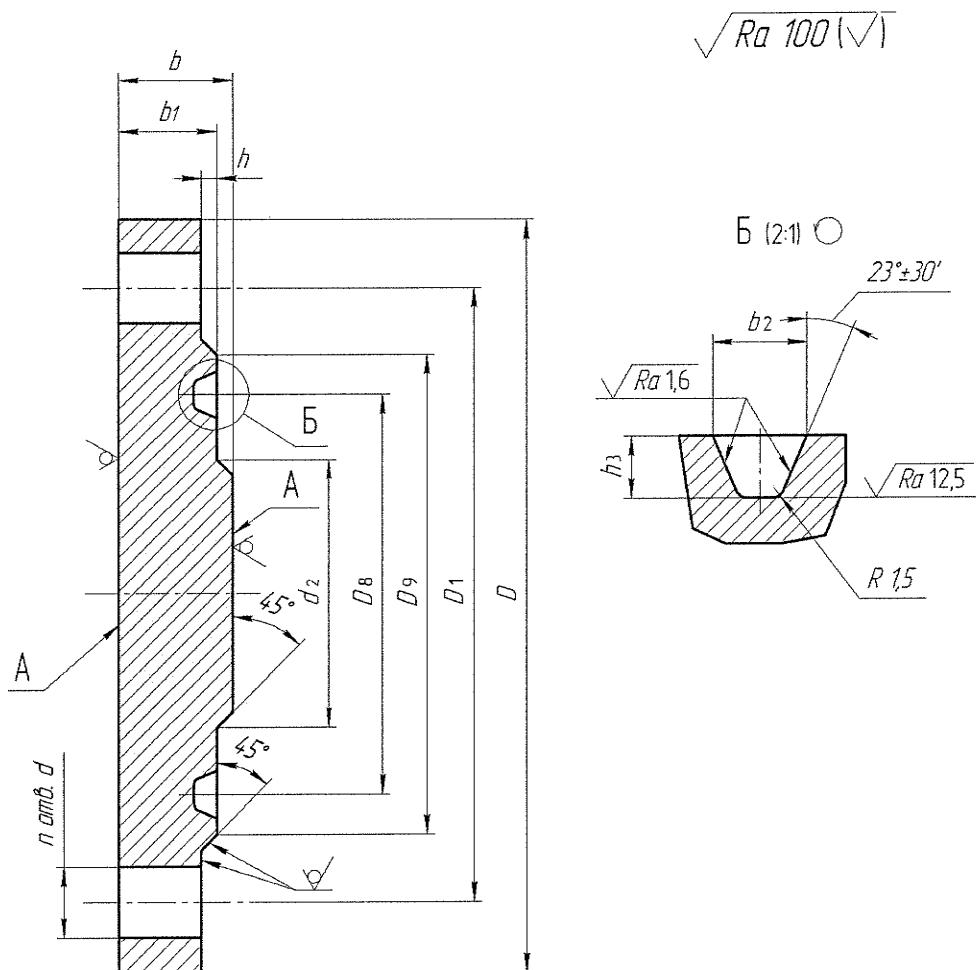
Конструкция и размеры заглушек с шипом (исполнение L) для фторопластовых прокладок
